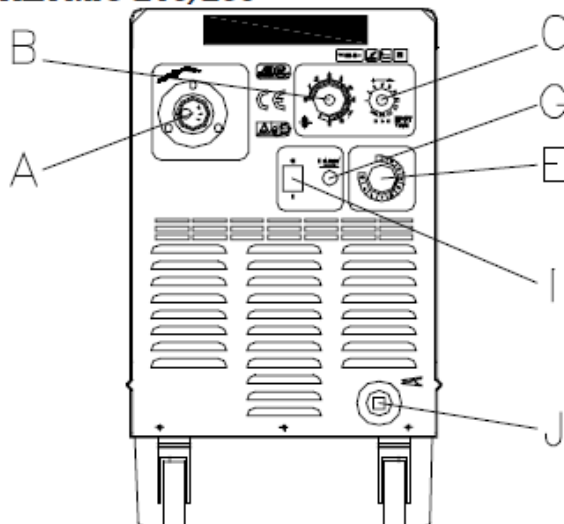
Máquina de soldadura Gala MIG 210.
